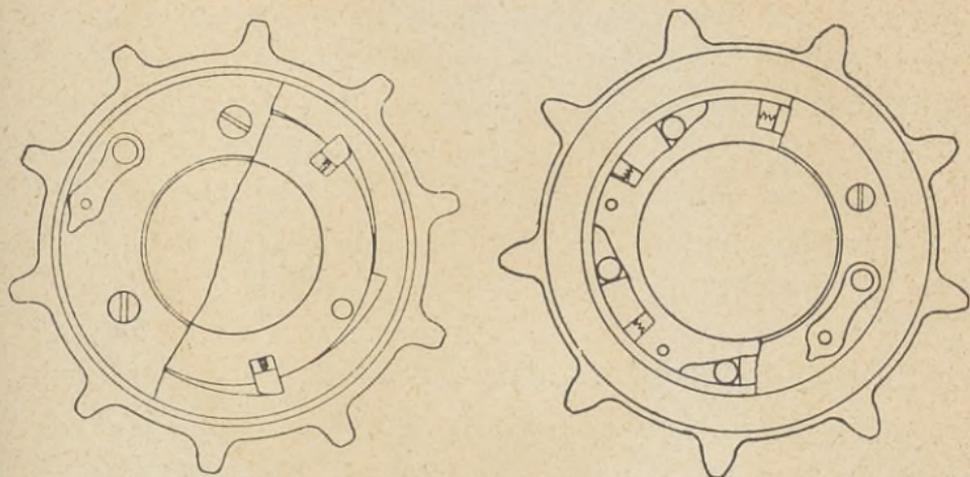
Freilaufvorrichtung in zwei verschiedenen Ausführungsformen.
